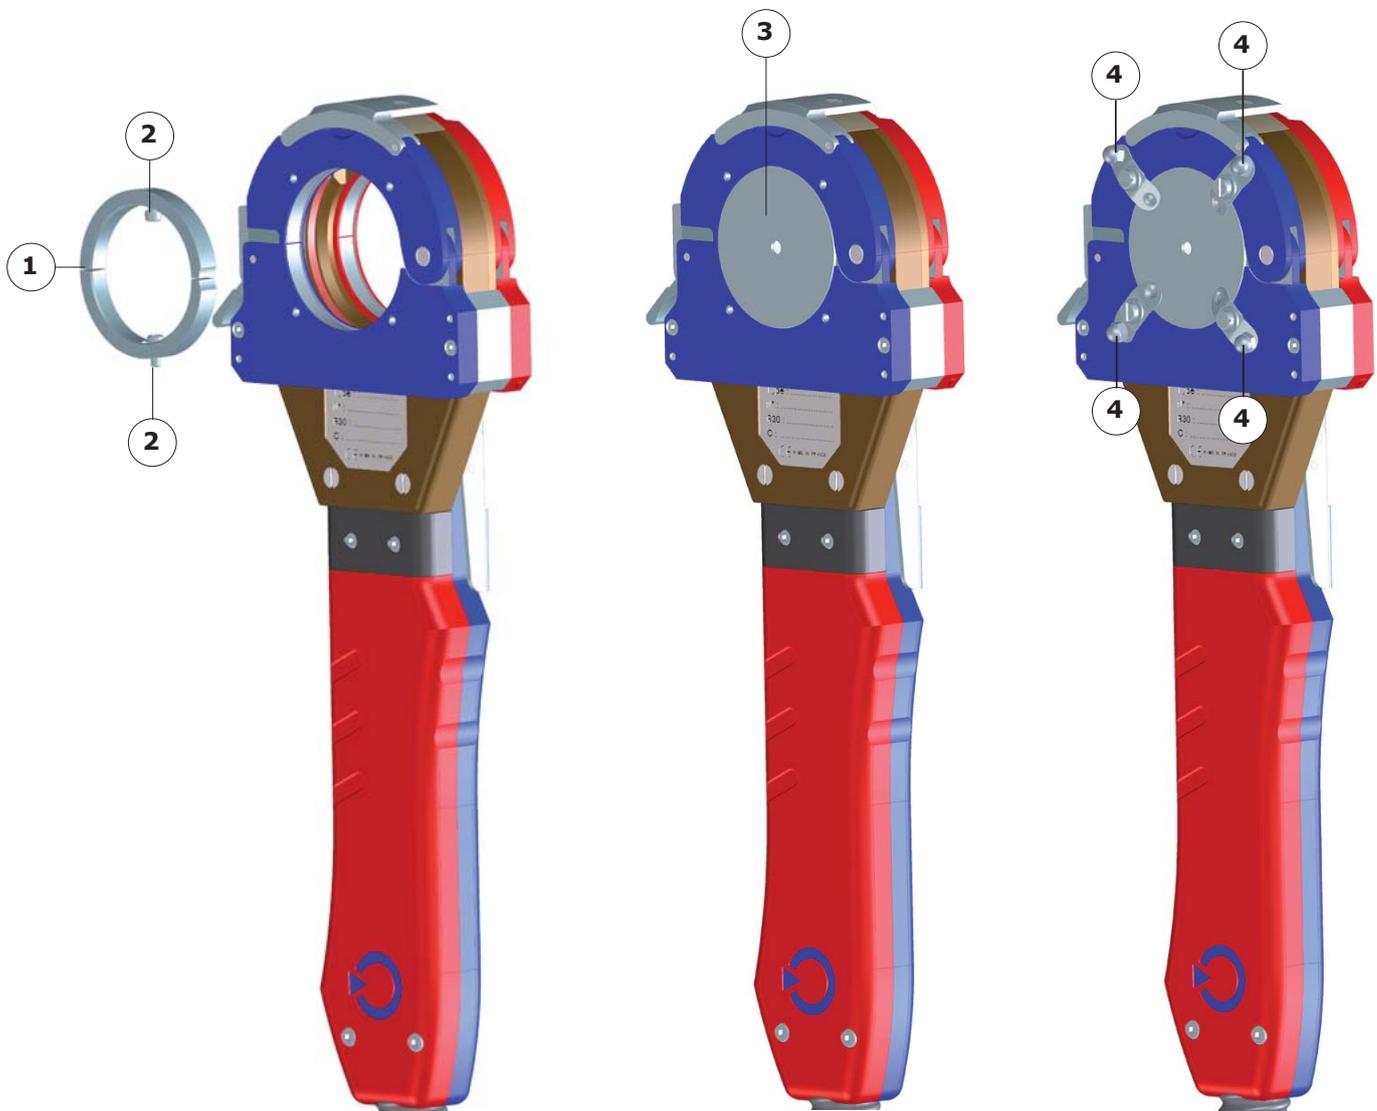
Montieren des Zubehörs zum Schweißen von Rohrbögen
